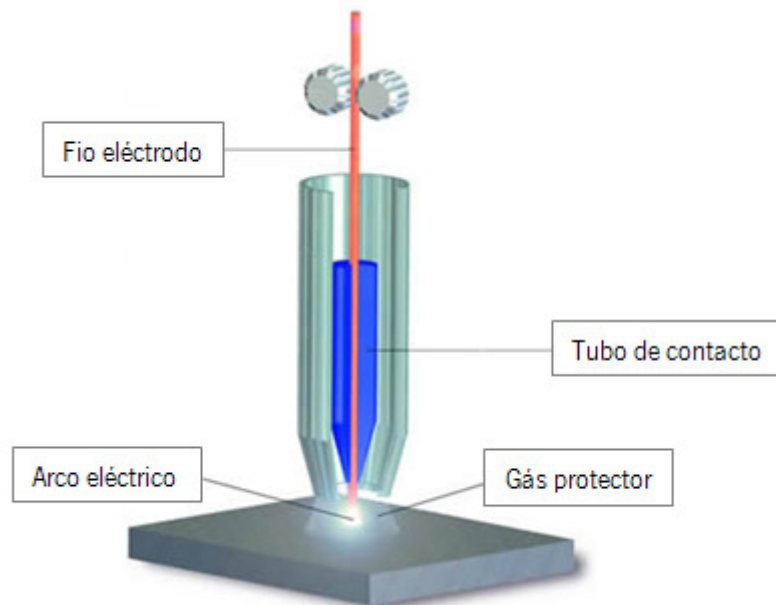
3 - Esquema representativo da soldadura MIG/MAG [10].
